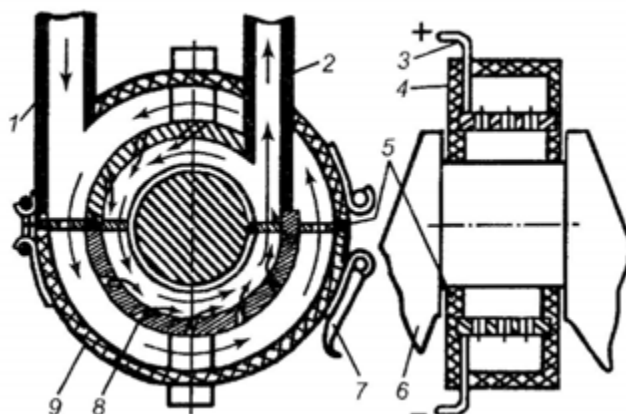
Схема пристрою для струменевого позаванного залізнення шийок валів: 1 – підвідний патрубков; 2 – відвідний патрубков; 3 – кабель; 4 – верхній корпус; 5 – ущільнювальна прокладка; 6 – відновлювана деталь; 7 – затиск; 8 – анод; 9 – нижній корпус
